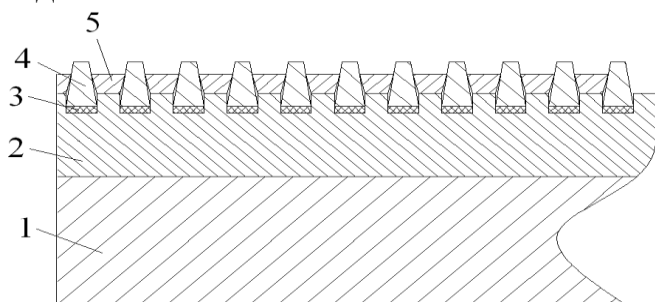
Схема гарнитуры с наборными ножами: 1–диск; 2–матрица; 3 – виброизолятор; 4 –нож; 5 –планка
